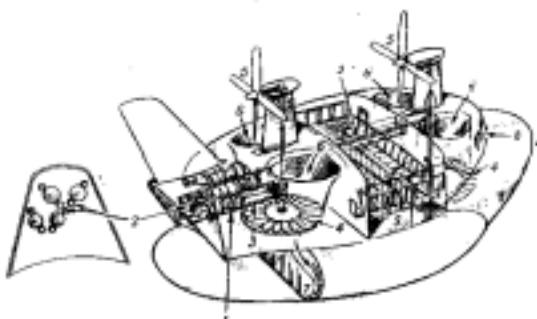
Схематический чертеж судна „Ховеркрафт СР-№ 2“.
